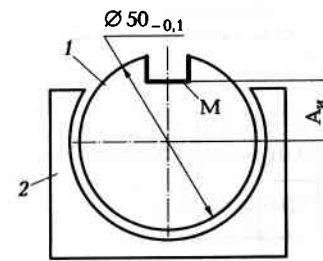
Схема установки заготовки в цилиндрическое отверстие при фрезеровании паза
